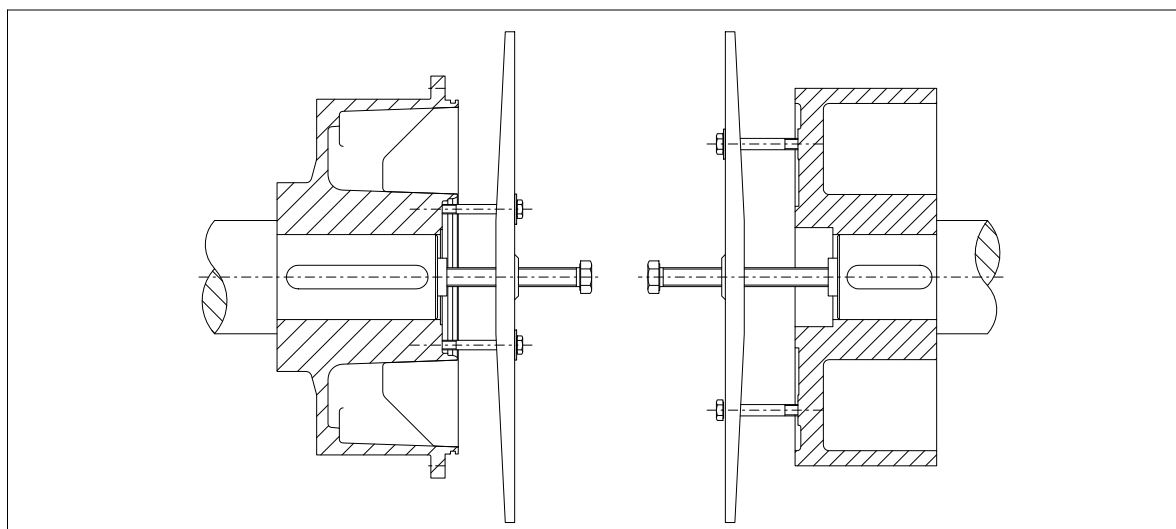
Desmontaje del acoplamiento FLUDEX -a
